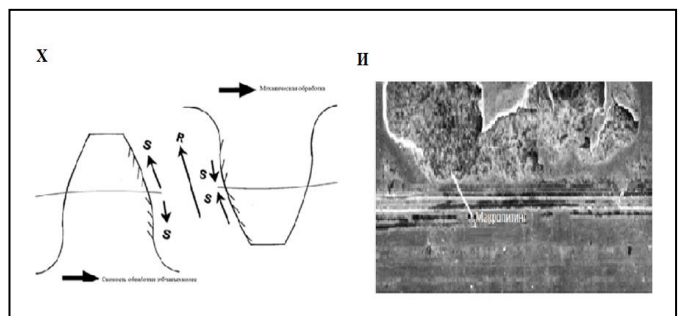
Изображение наложения на направления выступов (x) и скользяния (и) шероховатости поверхности зубчатых колес
